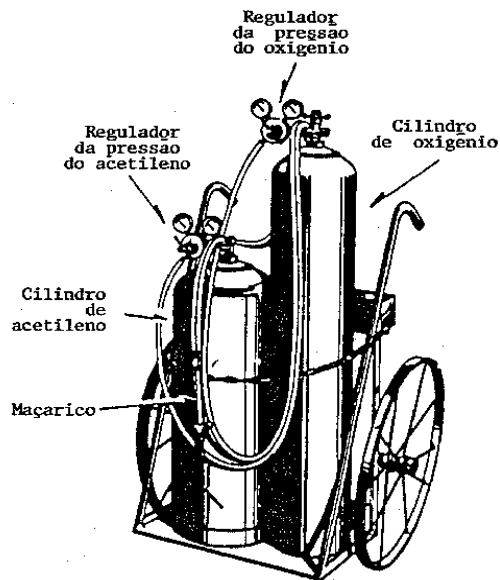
Equipamento portátil típico para soldagem com acetileno.
